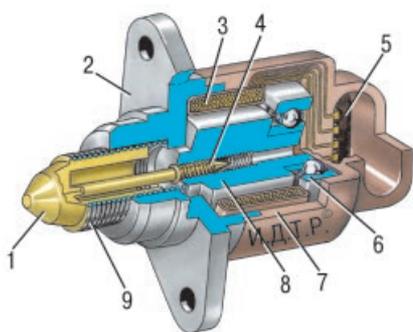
Регулятор холодного хода: 1 – клапан; 2 – корпус регулятора; 3 – обмотка статора; 4 – ходовой винт; 5 – штекерный вывод обмотки статора; 6 – шариковый подшипник; 7 – корпус обмотки статора; 8 – ротор; 9 – пружина
